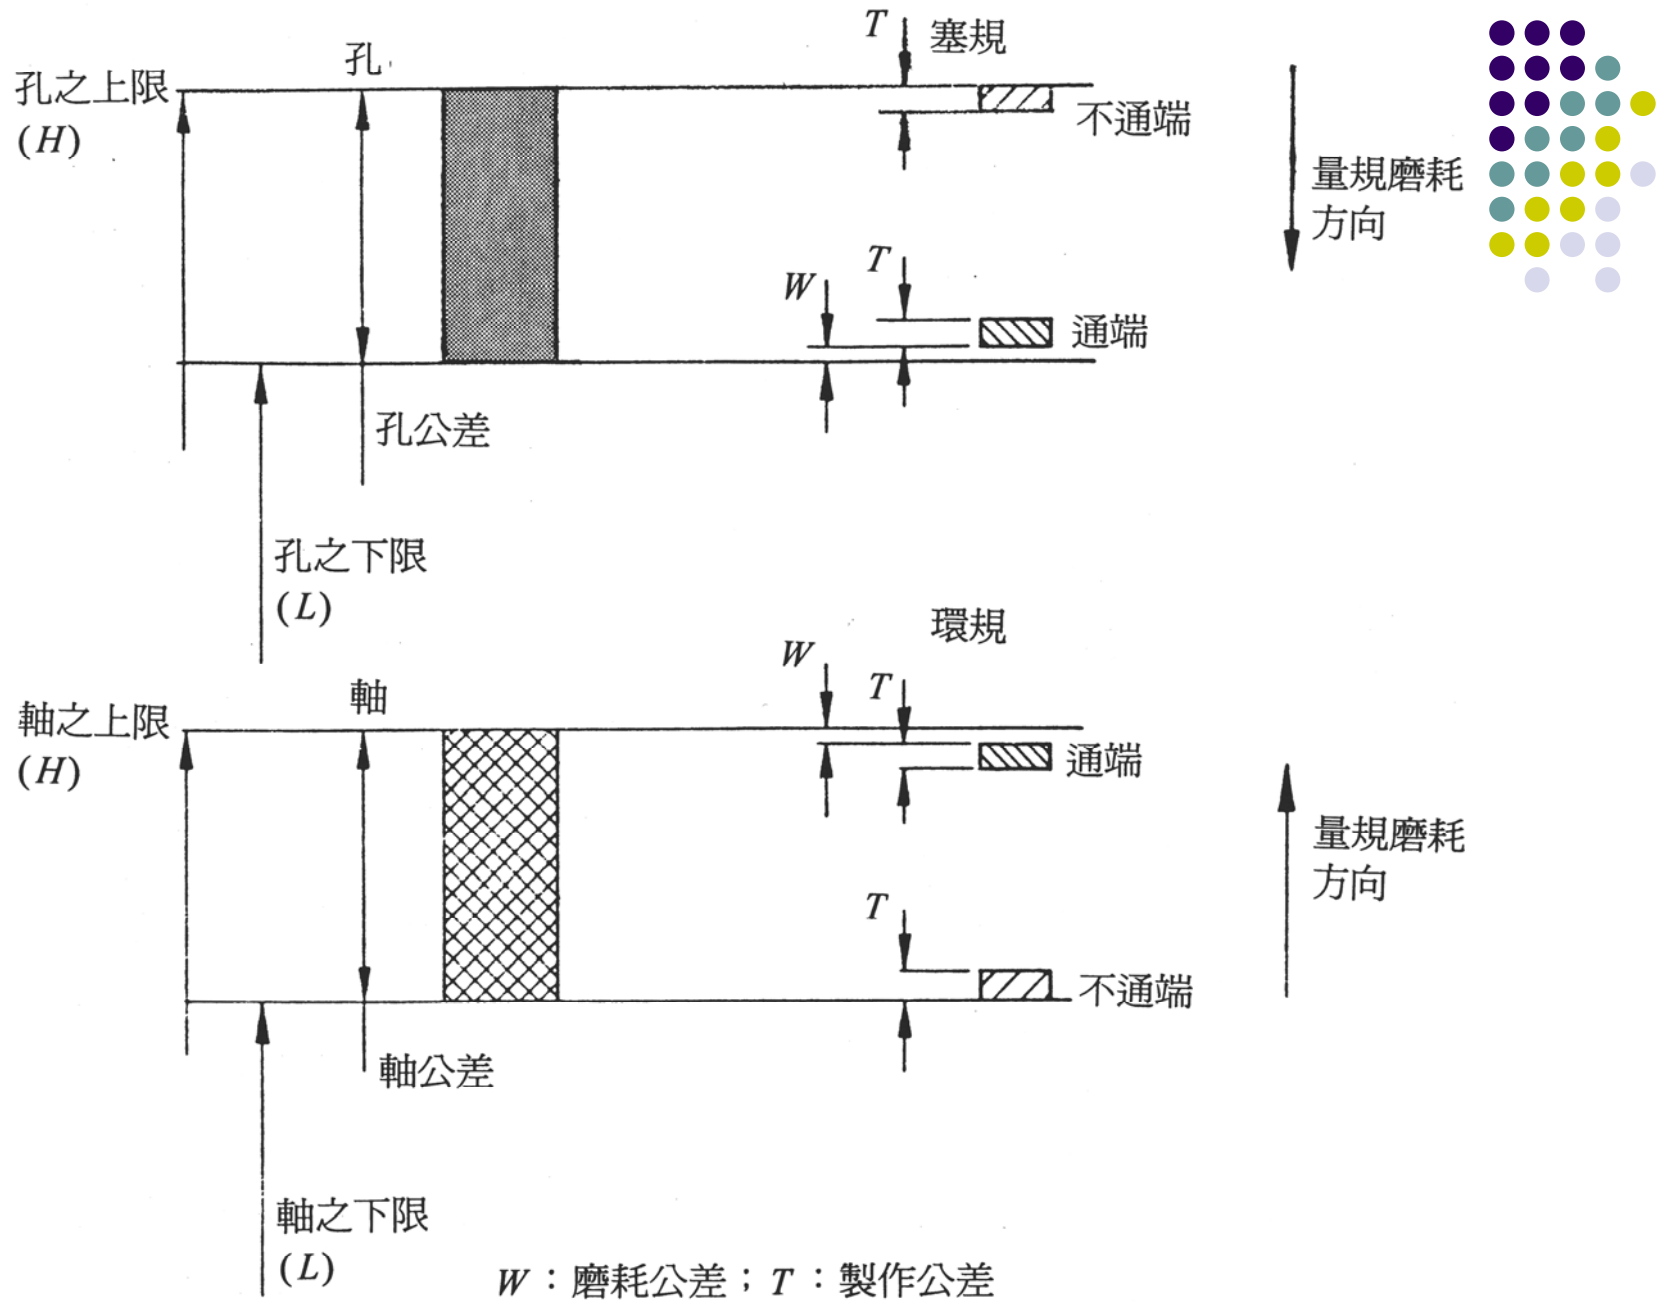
英國國家標準之工件公差與量規公差之相關圖 ([7], P.134)
